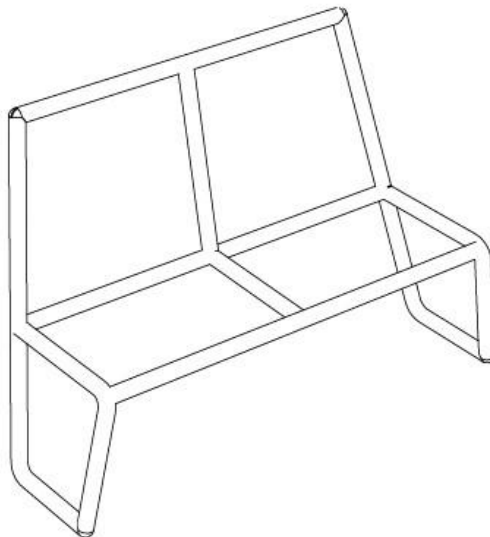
Esqueleto metálico do banco com laterais inclinadas
